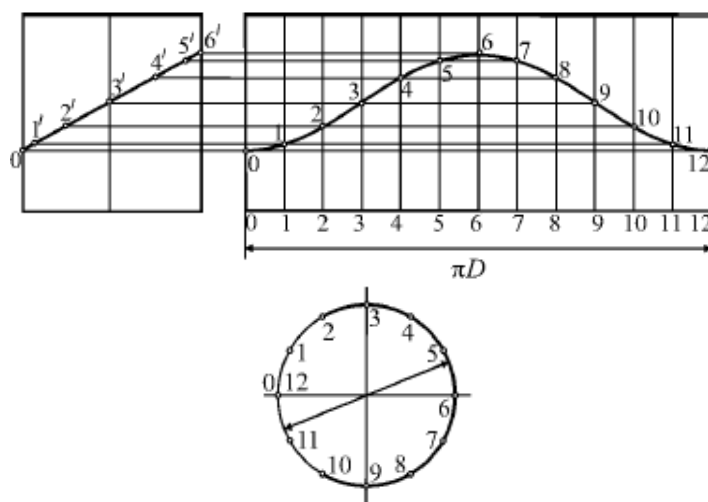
Построение развертки поверхности цилиндра и нанесение линии сечения
